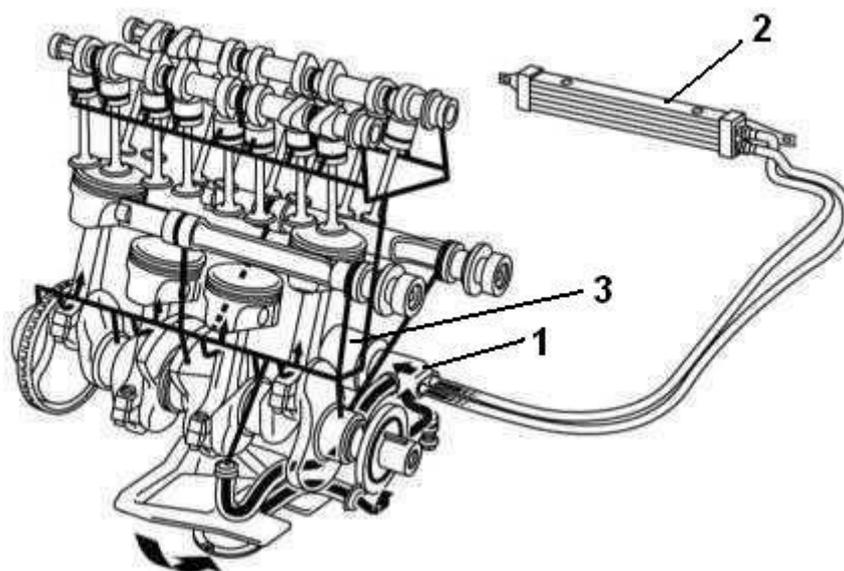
Система смазки двигателя с радиатором для охлаждения смазки
